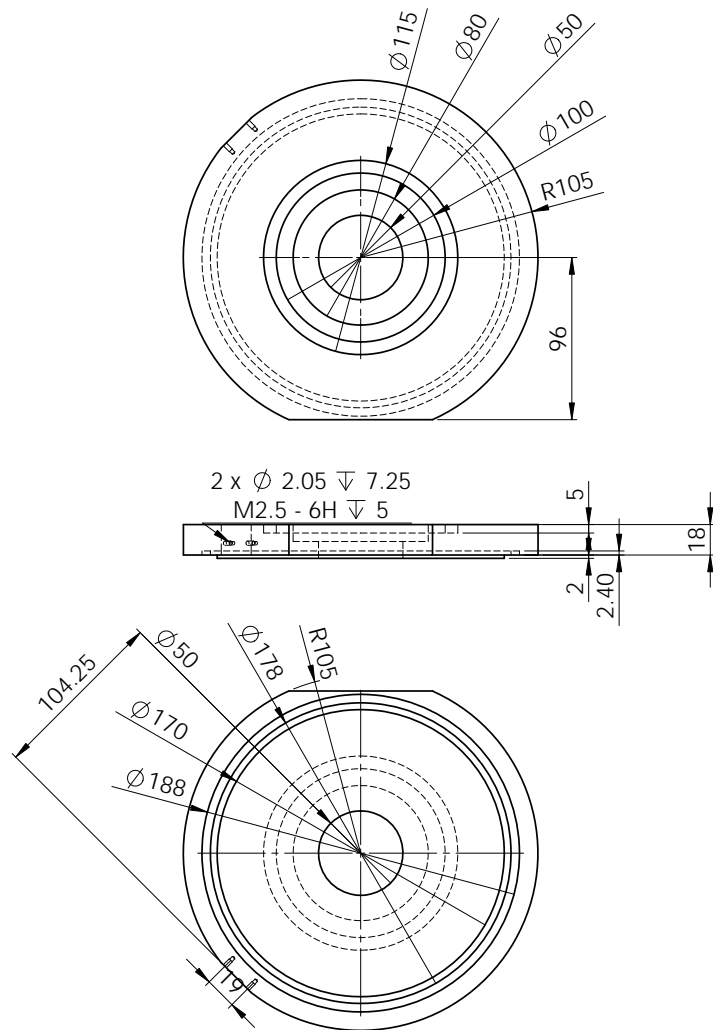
Technische Zeichnung des Deckels der Vakuumkammer.
